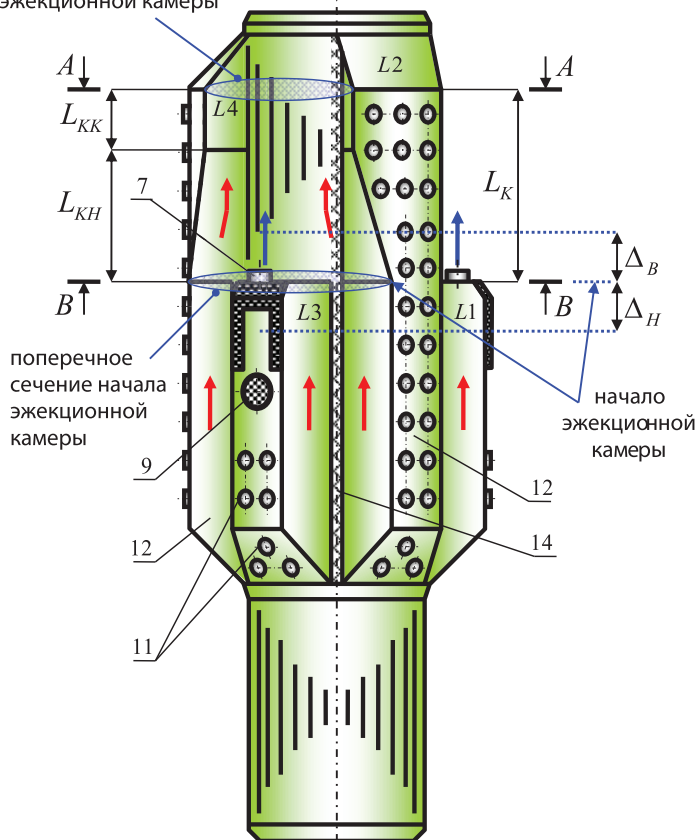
Общий вид корпуса наддолотного калибратора-эжектора
